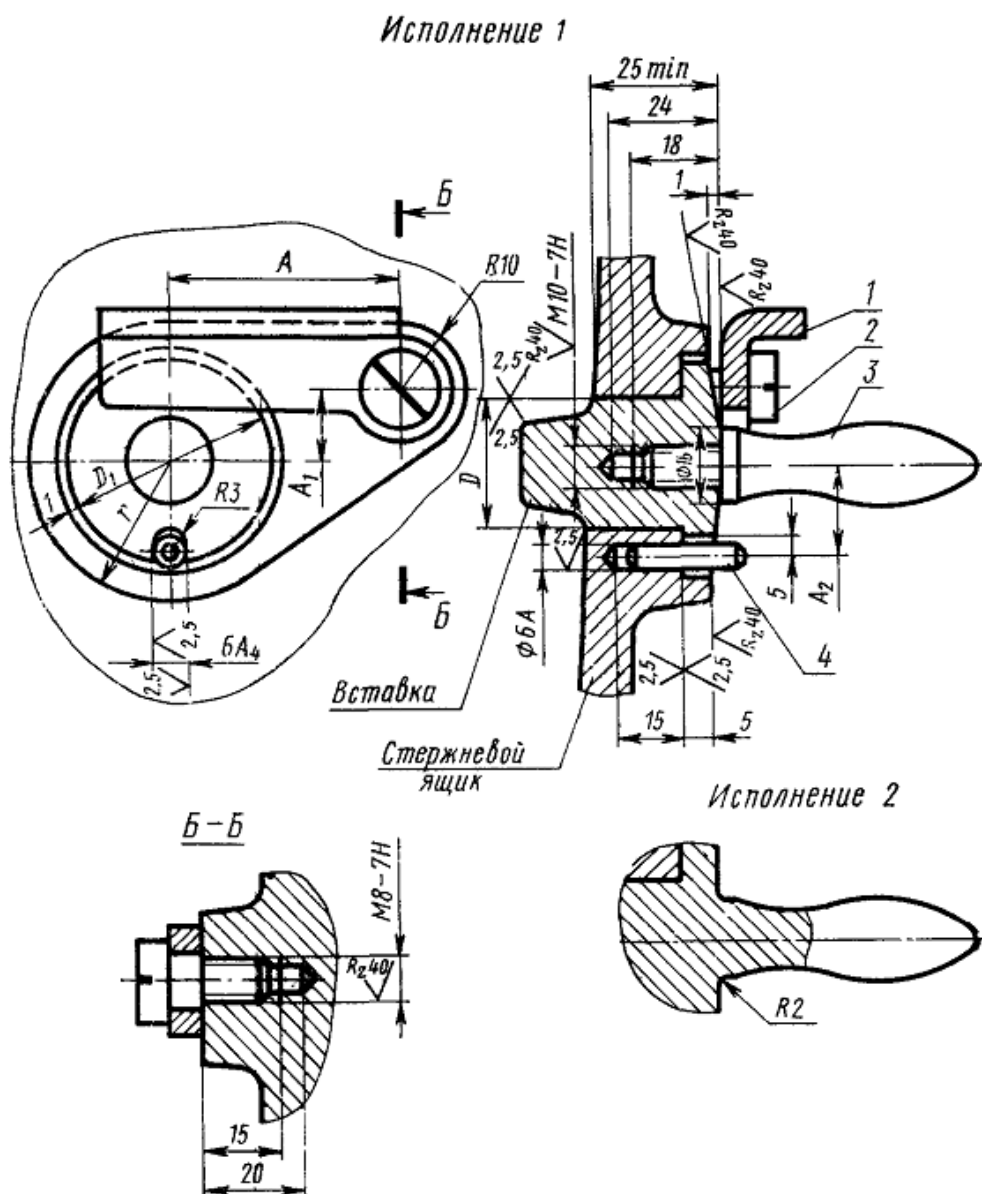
Конструкция и размеры вставки закрепляемой щеколдой
